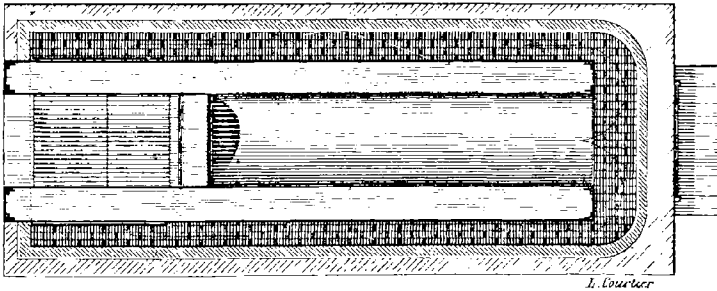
Chaudière de Cornouailles (coupe horizontale).
